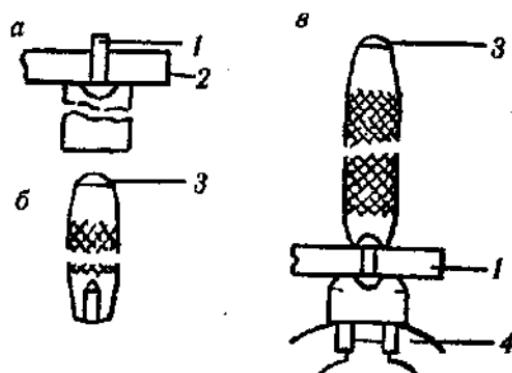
Инструменты для ручной клепки: а — поддержка; б — натяжка; в — обжимка; 1 — заклепка; 2 — соединяемые детали; 3 — ударная часть; 4 — тиски.
